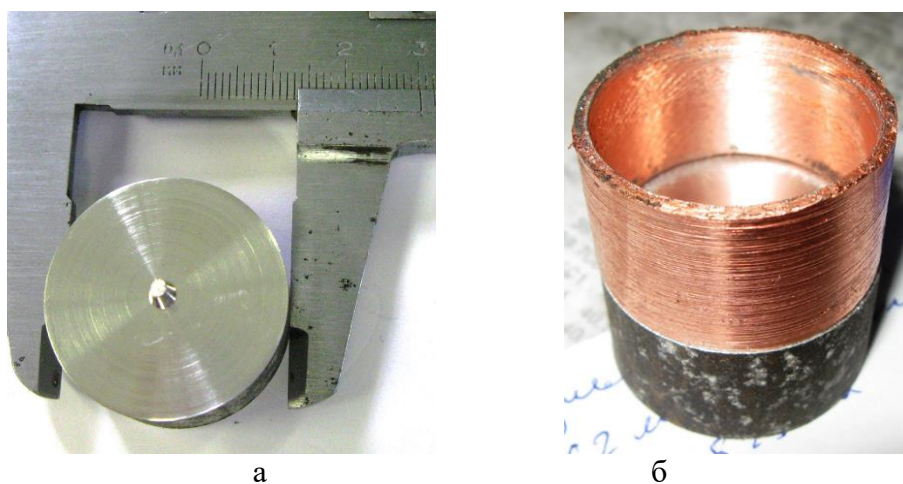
Цилиндрическая заготовка из сплава МА2-1 – а и медная обойма – б для создания противодействия
